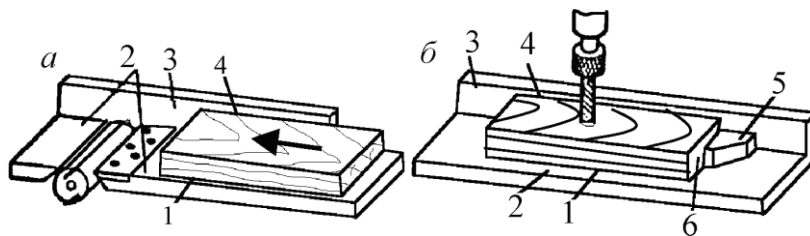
Базування деталі: а - рухоме; б - нерухоме
